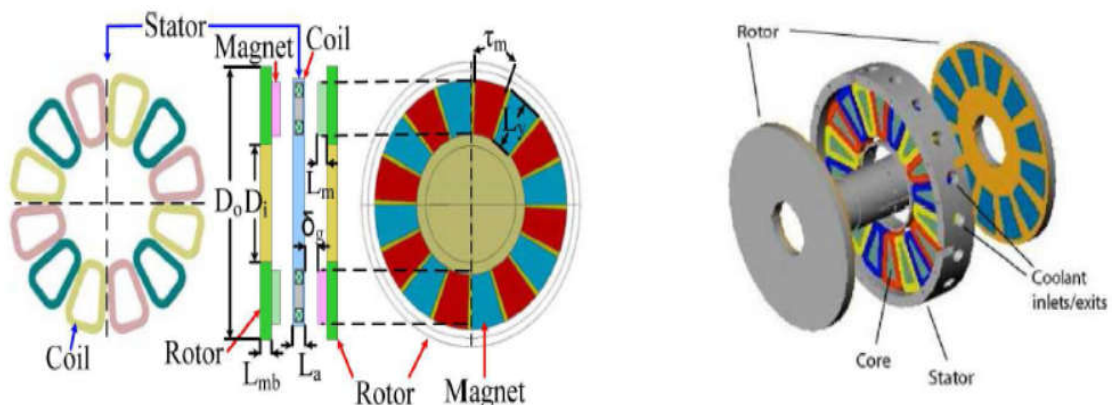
Machine à flux axial à bobinage sur dents 1 stator / 2 rotors[12].
